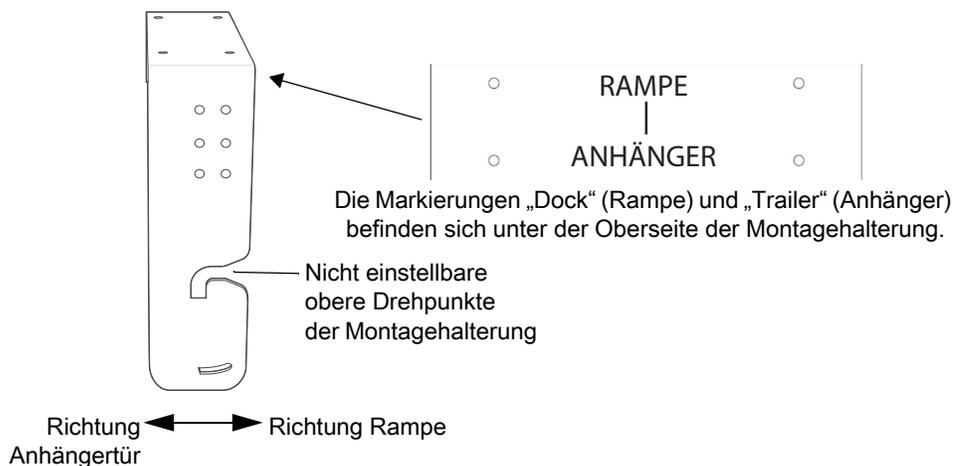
Stange AS-000341-01 mit der befestigten Halterung BI-000237-01-TLA
